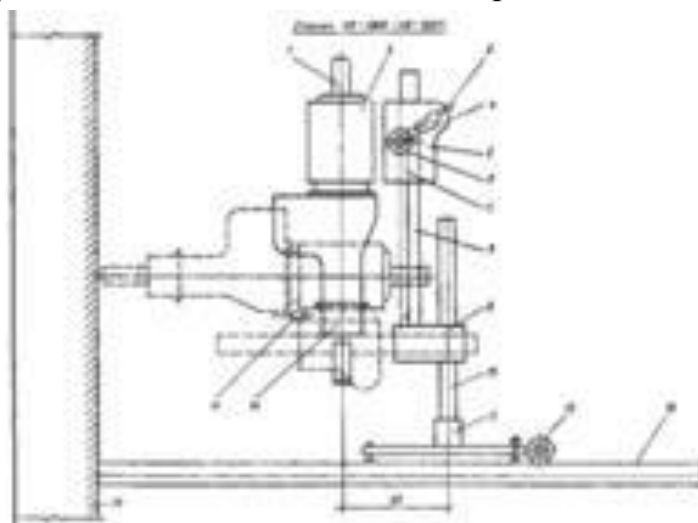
Сверлильный станок типа ИЭ 1806
